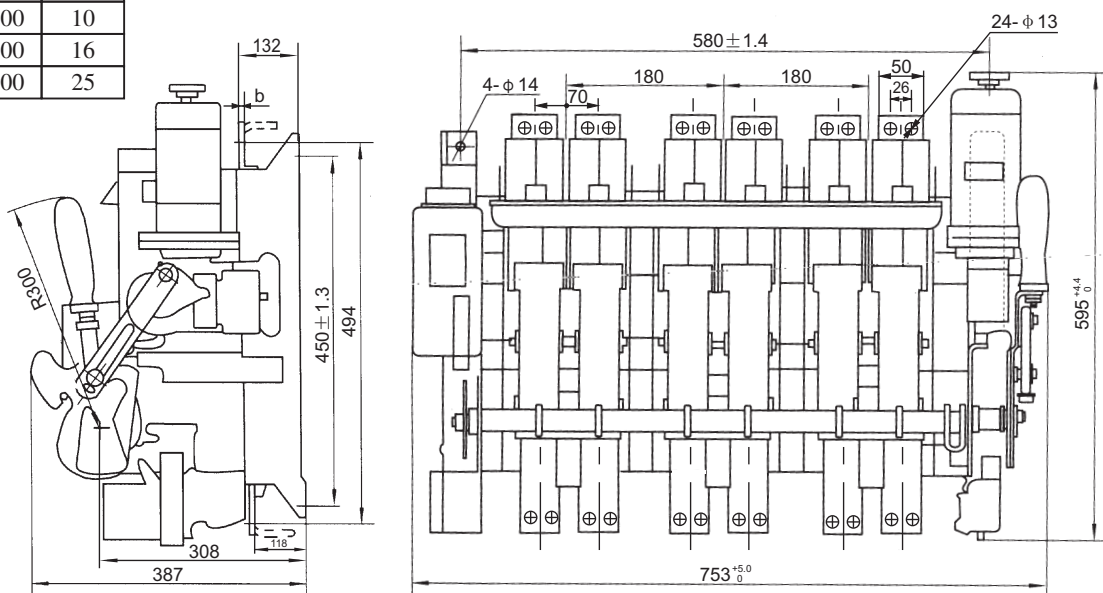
DW16-4000断路器的安装尺寸和外形尺寸 (可替换DW10-2500A安装及外形尺寸)
